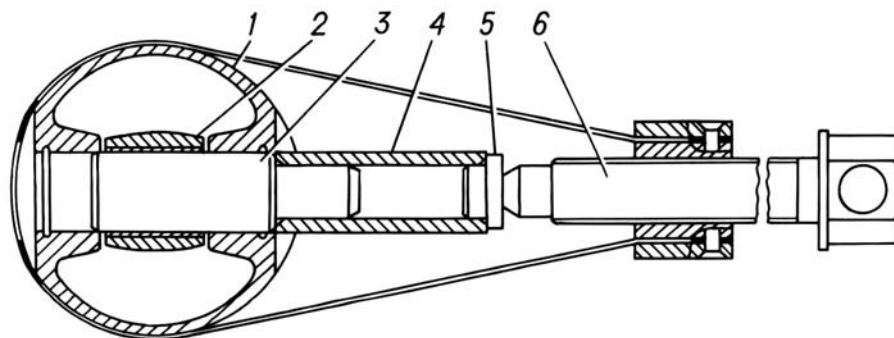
Запрессовывание поршневого пальца в поршень и шатун при помощи приспособления: 1 - поршень; 2 - шатун; 3 - оправка; 4 - палец; 5 - подпятник; 6 - винт
